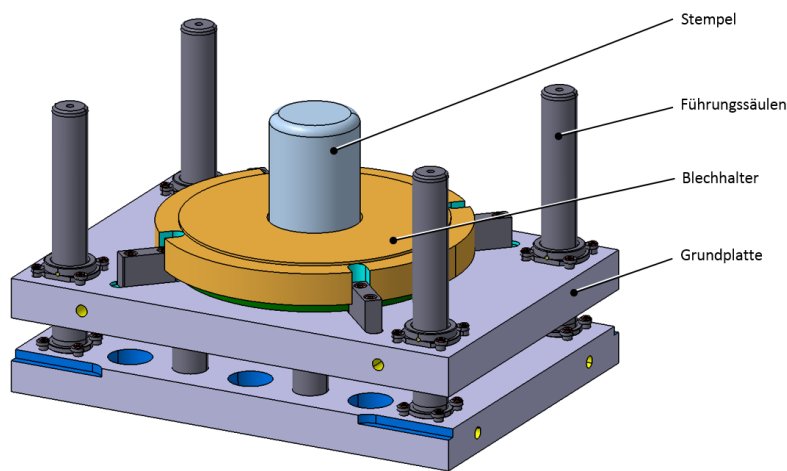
Unterwerkzeug mit Stempel und Blechhalter
